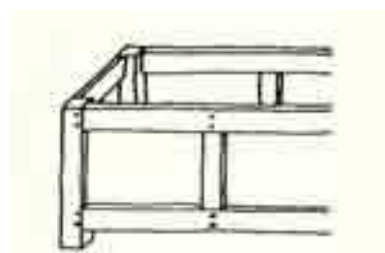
Construção do móvel com juntas encaixadas e fixadas com espigas de madeira.
